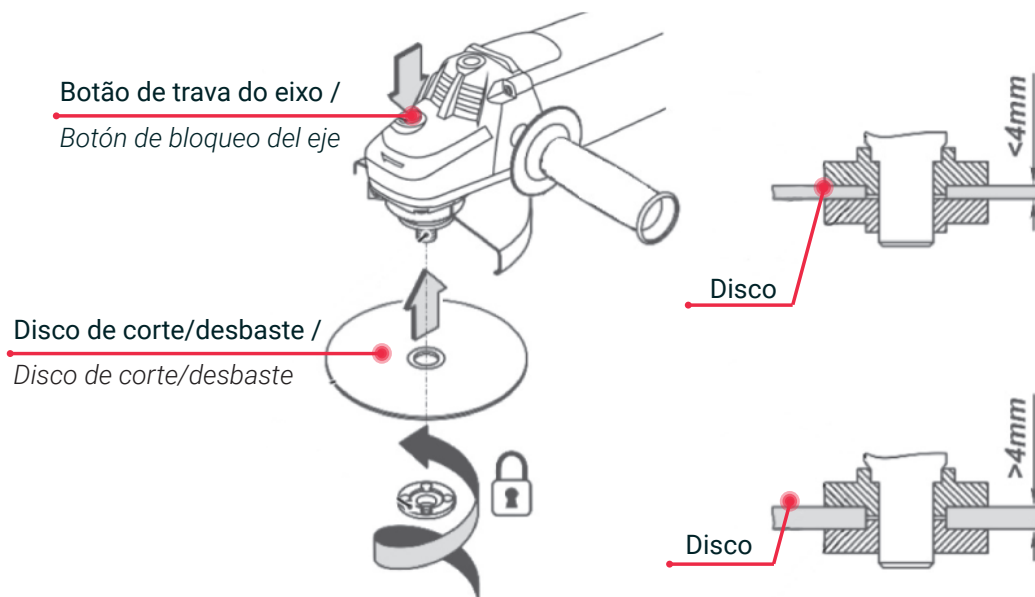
Montagem de acessórios na máquina / Montaje de accesorios en la máquina
